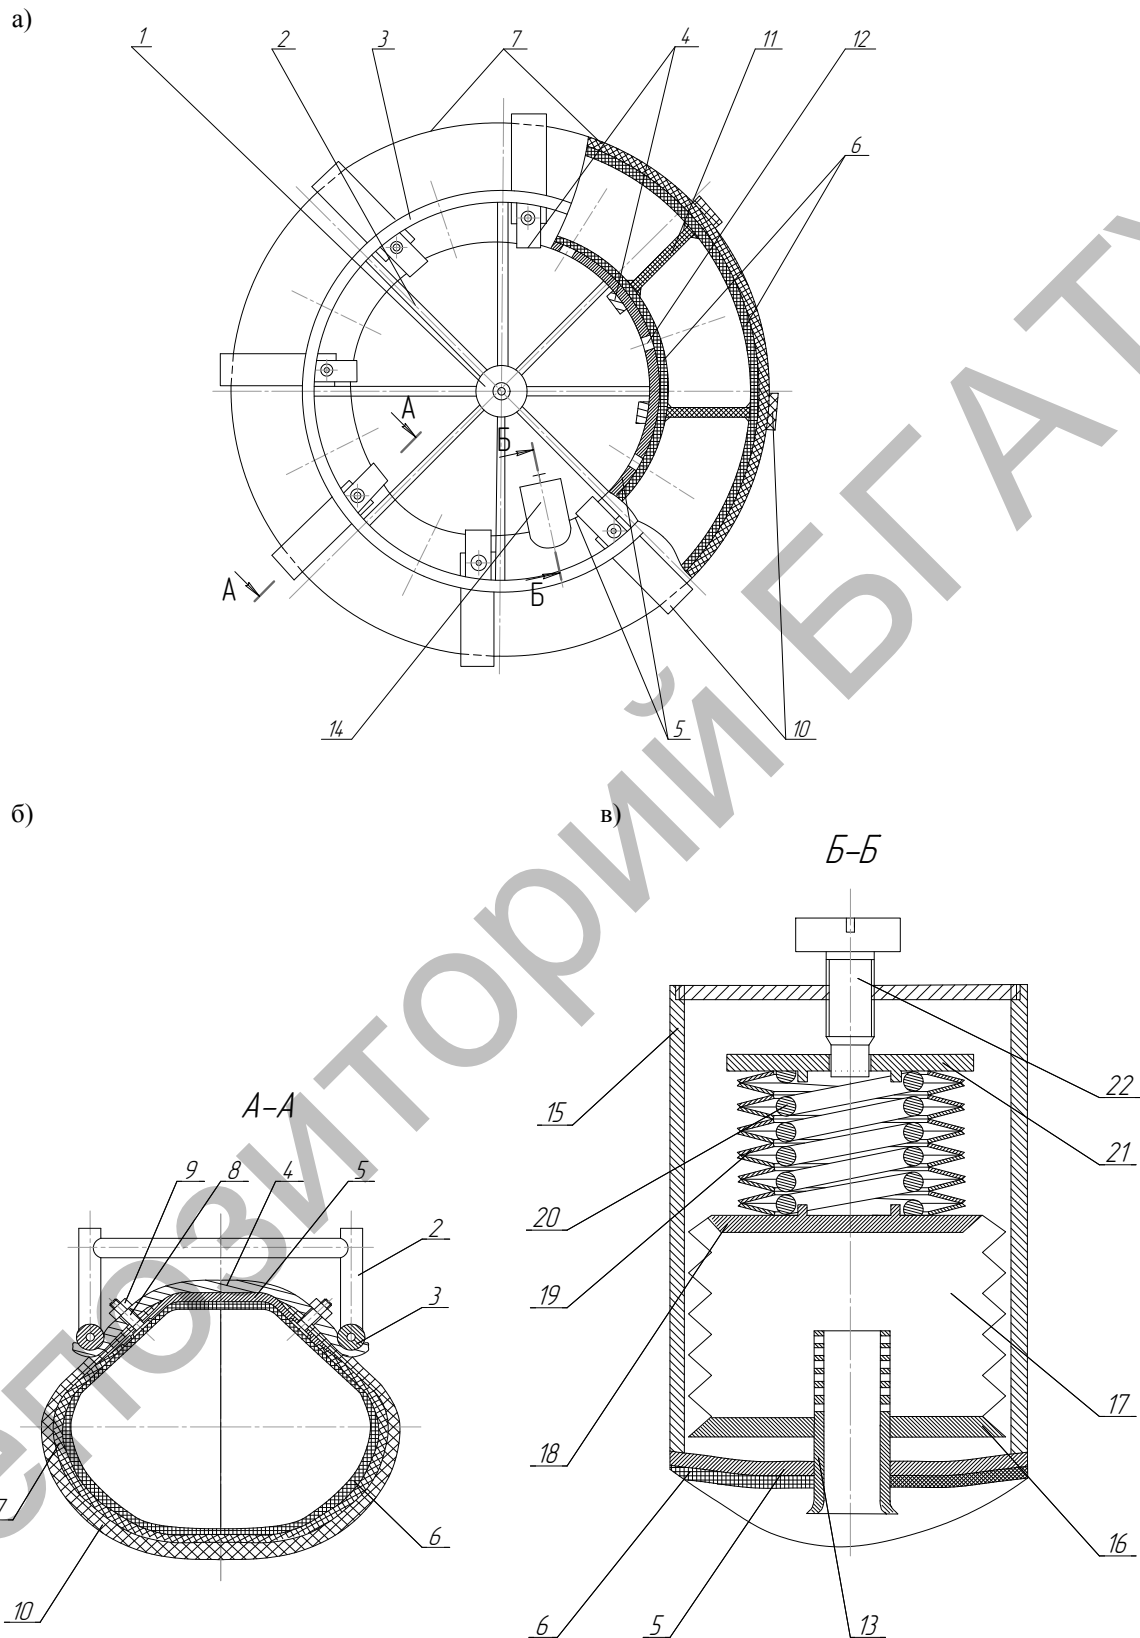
Колесо низкого давления и повышенного демпфирования: а – общий вид колеса сбоку, выполненный с разрезом; б – разрез А-А; в – разрез Б-Б
